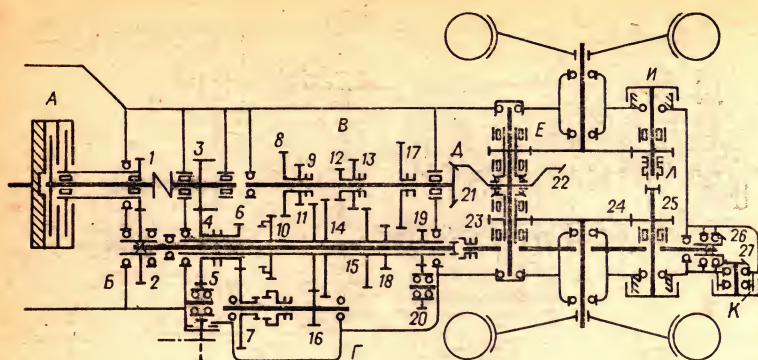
Кинематическая схема силовой передачи трактора ЮМЗ-6: А — двухшестеренная муфта сцепления; Б — привод к ВОМ; В — коробка передач; Г — редуктор-удвоитель; Д — центральная передача с дифференциалом; Е — конечная передача; И — колодочный тормоз; К — приводной шкив; Л — муфта блокировки дифференциала
